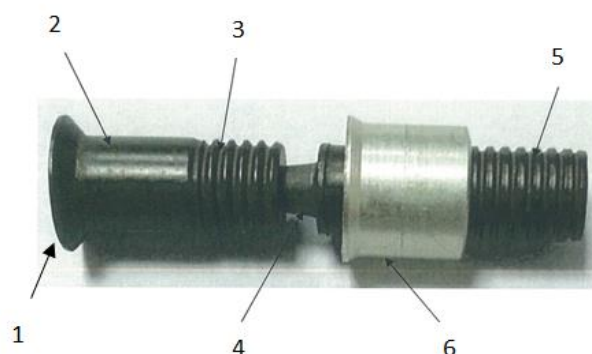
Конструкция болт-заклепки с технологическим хвостовиком до выполнения соединения: 1 - закладная головка; 2 - гладкая часть; 3 - цилиндрическая часть с кольцевой накаткой; 4 - шейка; 5 - хвостовик с кольцевой накаткой, 6 - кольцо
